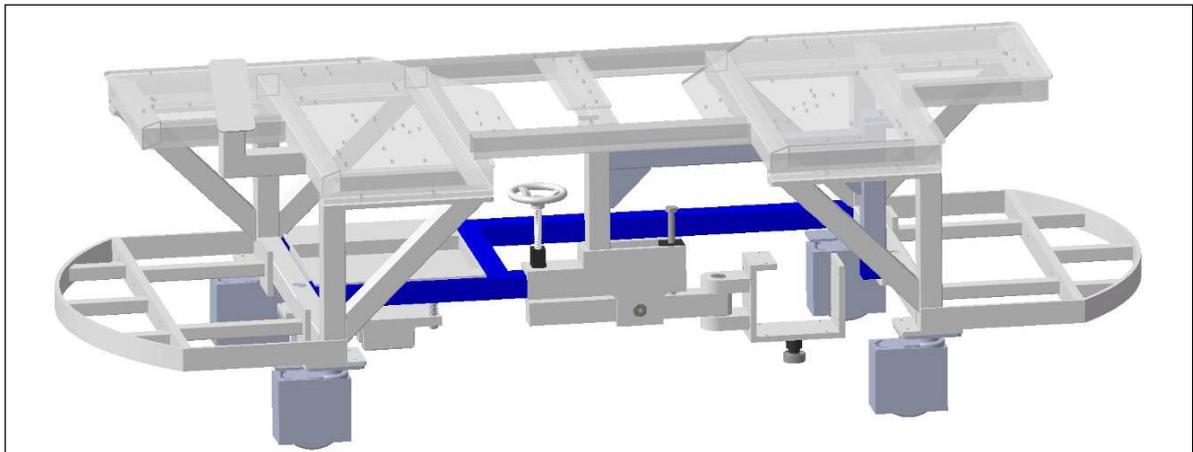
Reforço estrutural destacado em azul (Fonte: autoria própria).
